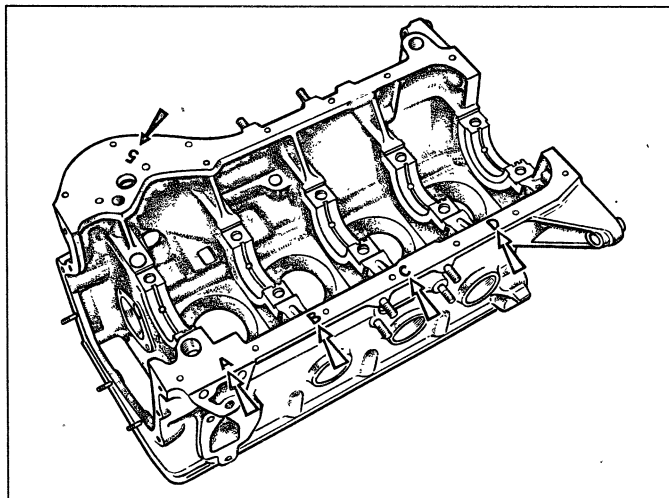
Маркировка размерного класса цилиндров на блоке
